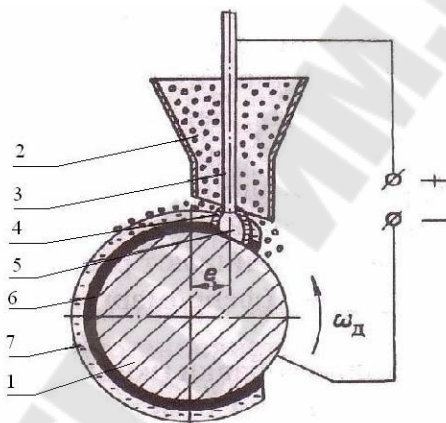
Наплавка цилиндрической детали под слоем флюса: 1 – изделие; 2 – бункер с флюсом; 3 – электродная проволока; 4 – расплавленный флюс (шлак); 5 – сварочная дуга; 6 – наплавленный слой; 7 – шлаковая корка
